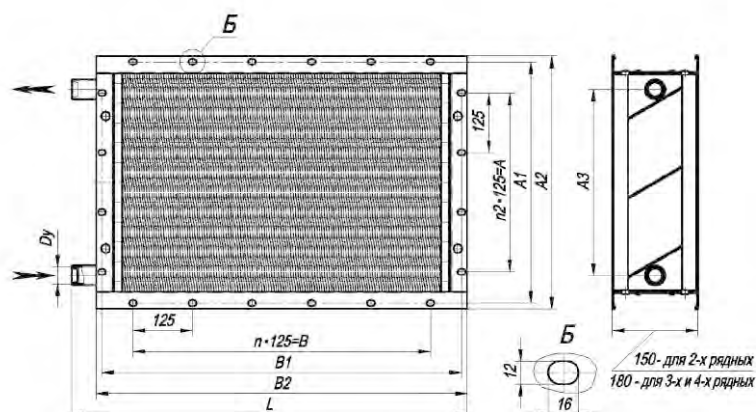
Габаритные и присоединительные размеры calorifера типа КСк.
